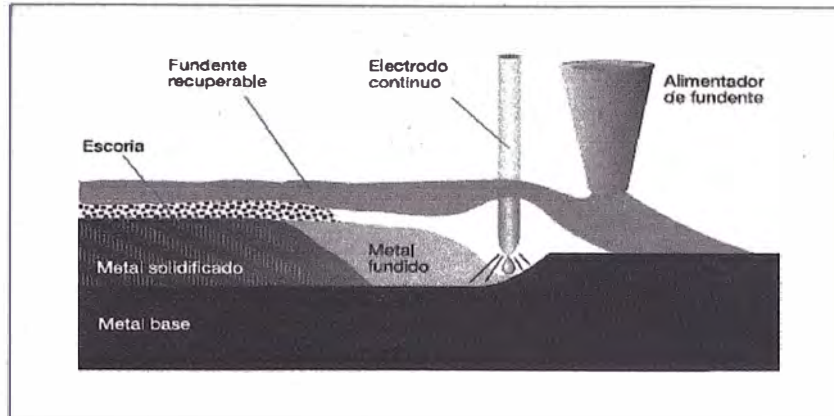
Esquema Proceso SAW (Fuente: Manual de Soldadura Indura)
